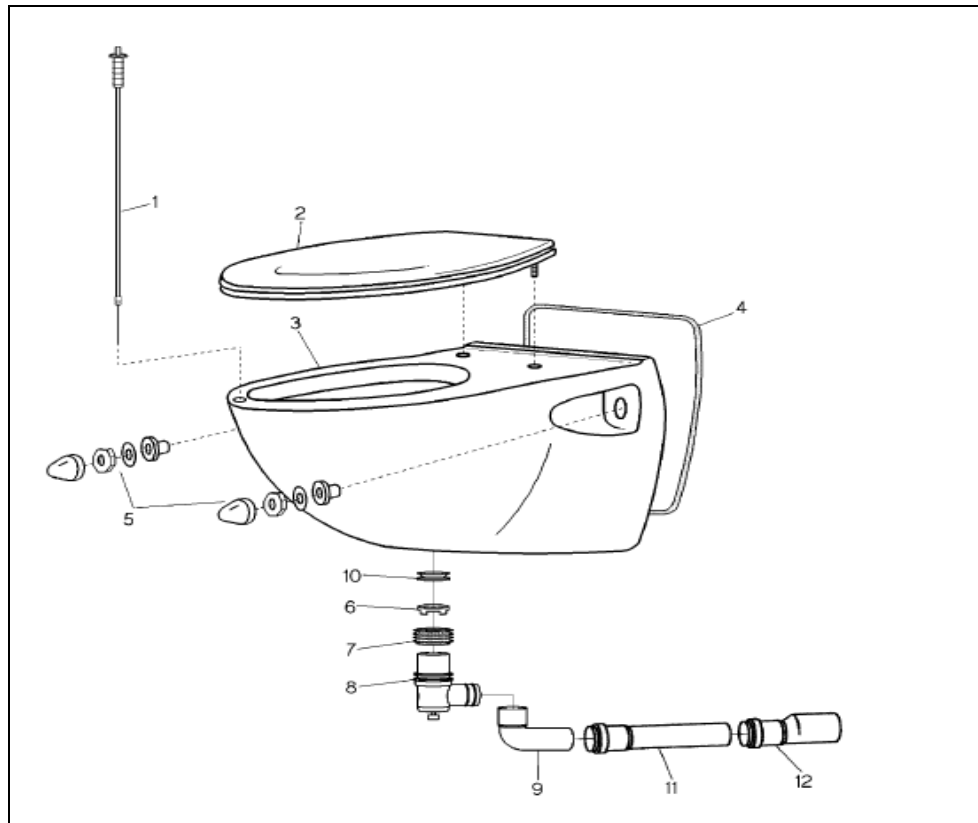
Explosionszeichnung der NoMix-Toilette.
